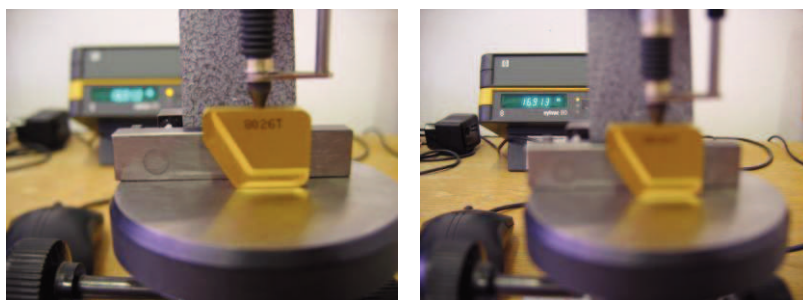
Prototypová výrobní dávka hladících VBD typ SNKR 1706DZSR; 8026T
